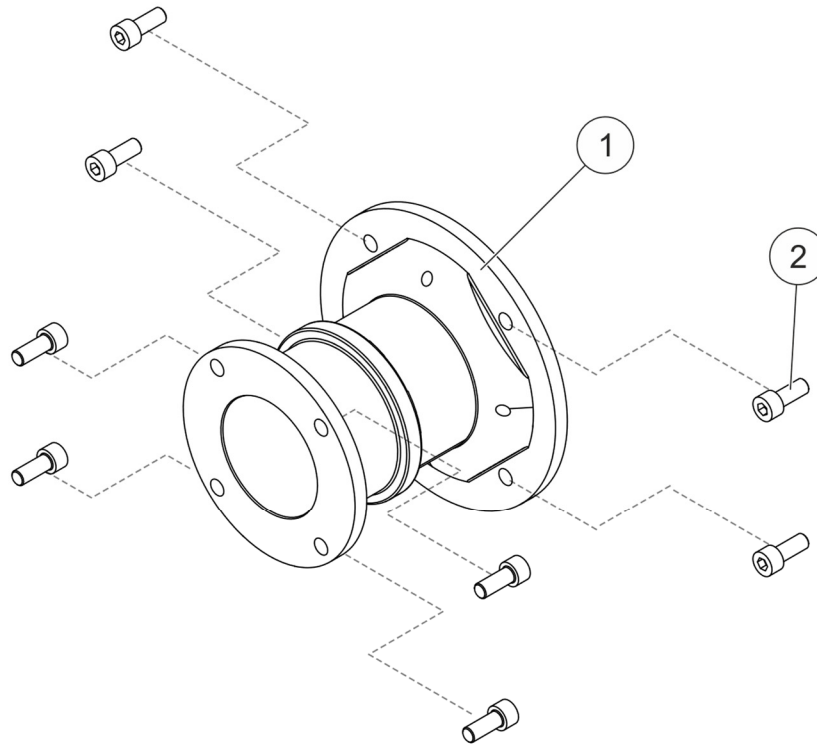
Baugruppe Motorflansch PQ25T-EX
